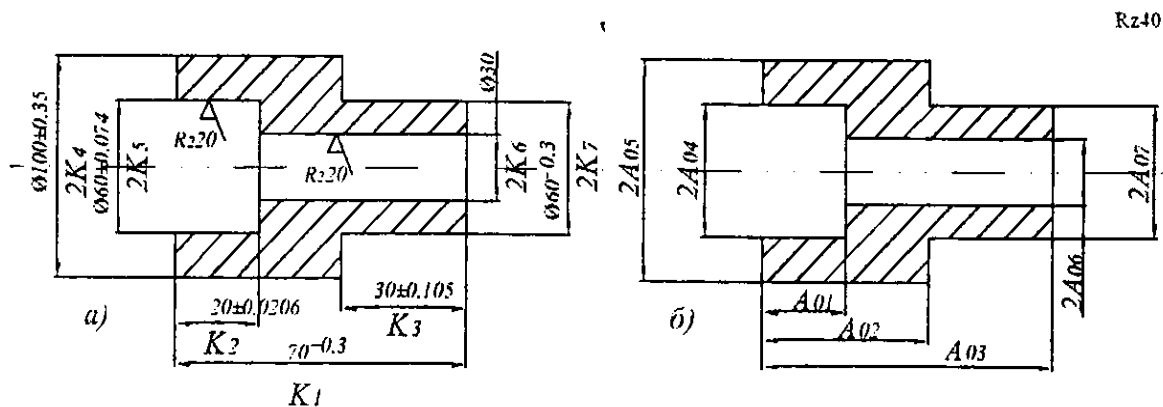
Креслення цапфи: *а* – ескіз деталі; *б* – ескіз заготовки
